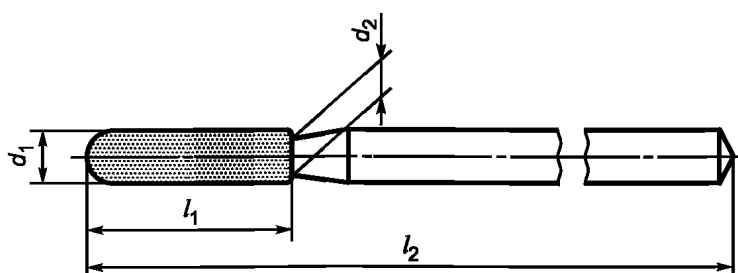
Цилиндрическая полусферическая рабочая часть с длиной головки 8,0 мм
